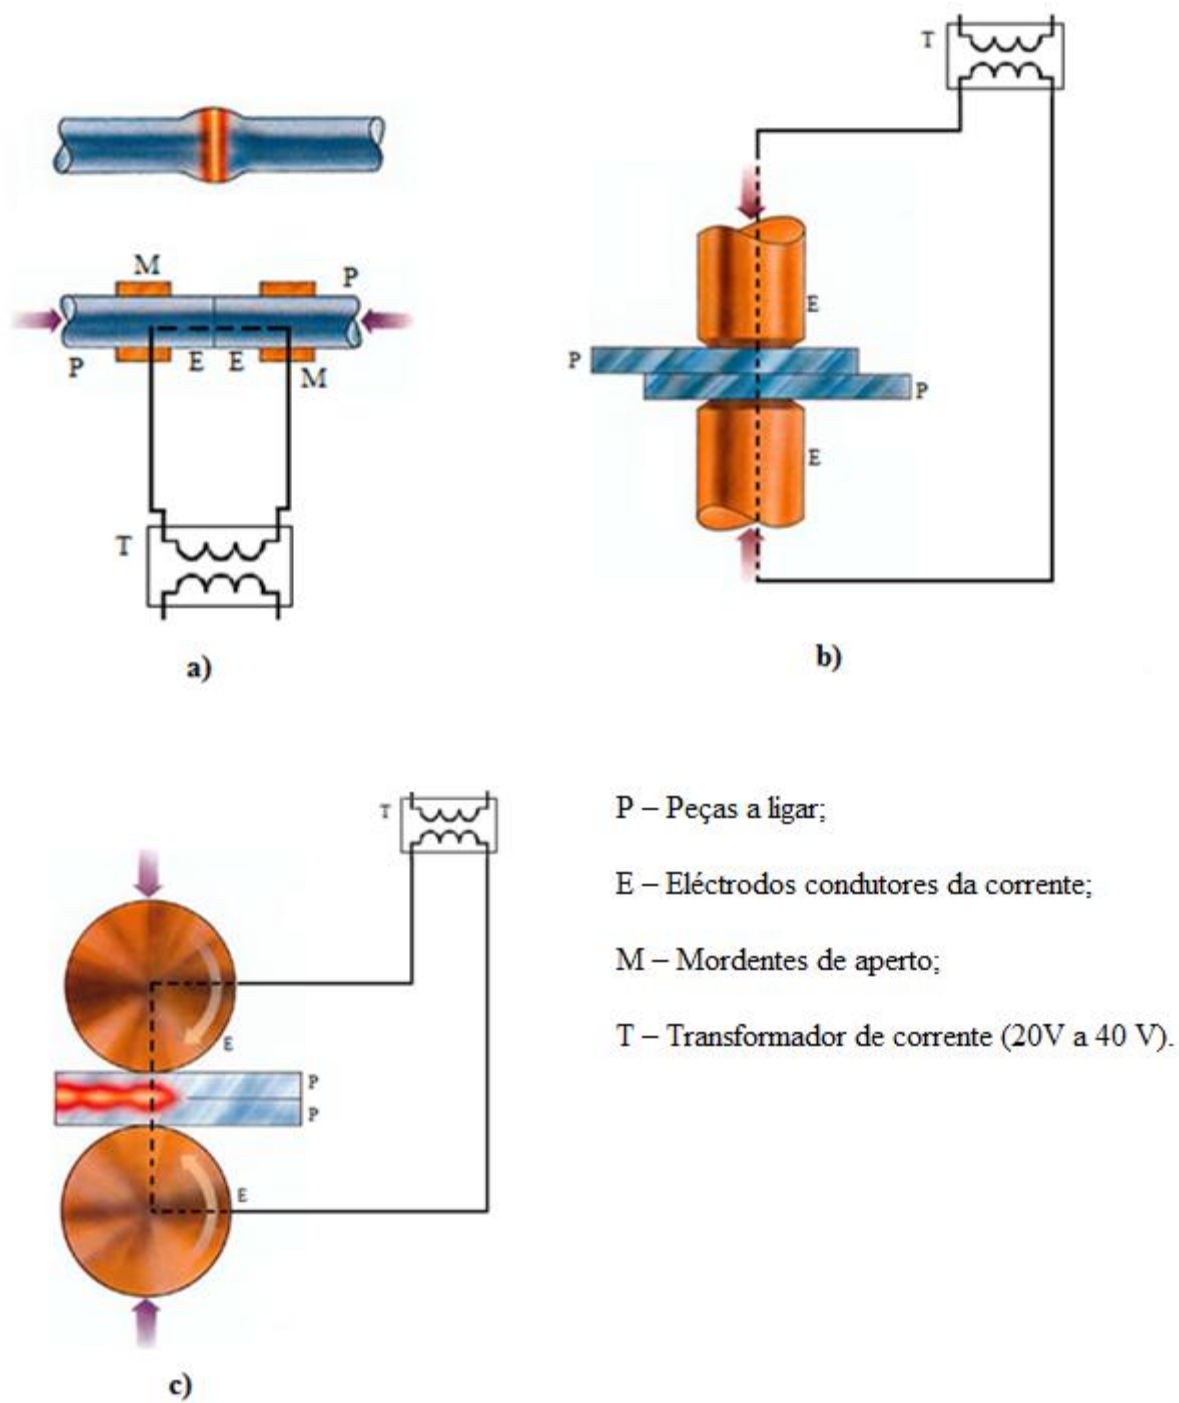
Soldadura por resistência. a) de topo; b) por pontos; c) por costura
